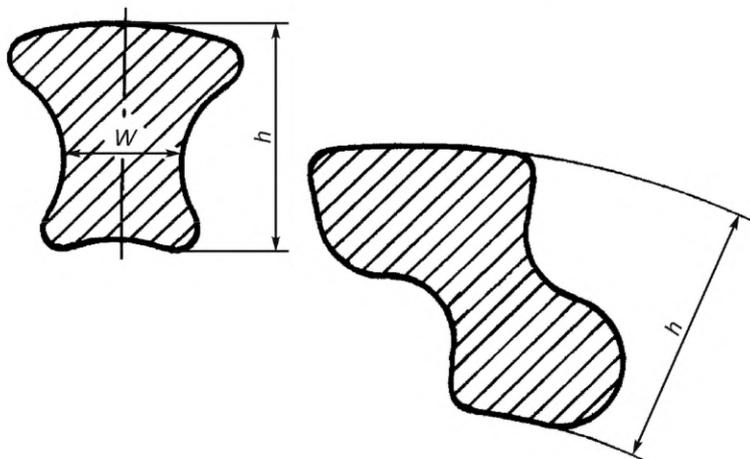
Сечения проволоки полностью закрытой и полузакрытой конструкций
